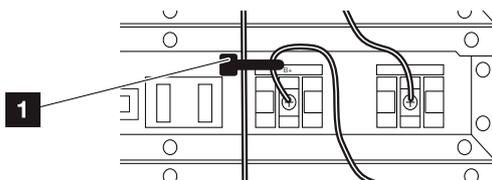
Befestigung DC-Leitung mit Kabelbinder
